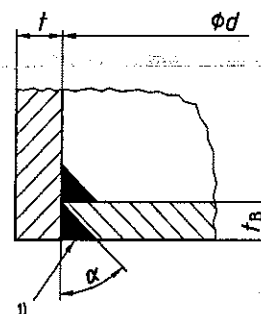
Schweißverbindung zwischen Tankwand und Boden
